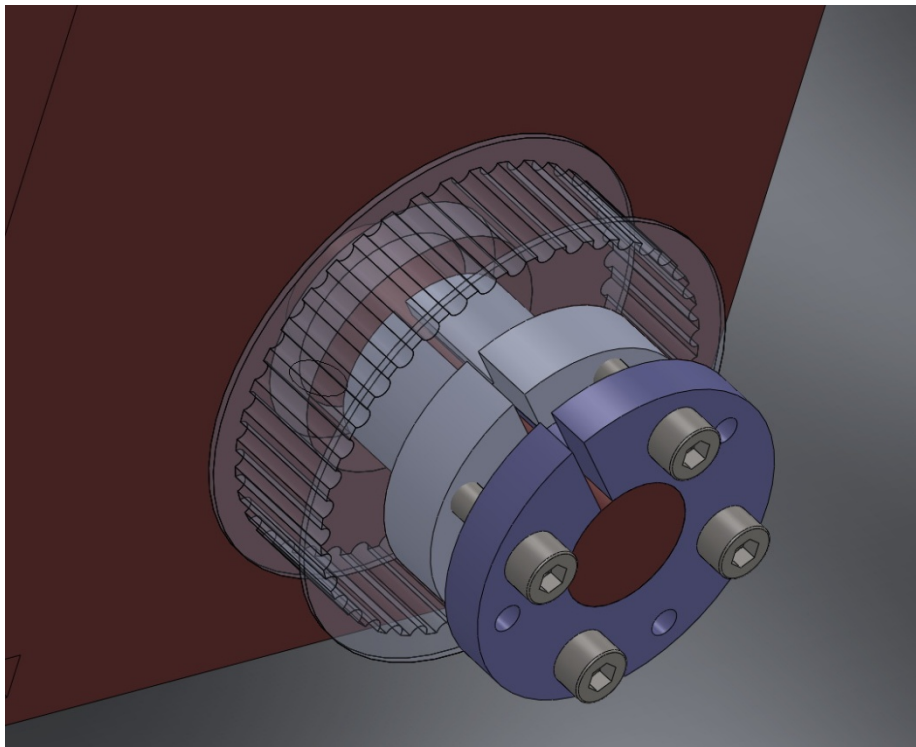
Sestavljena prosto vrteča-se zobata jermenica
